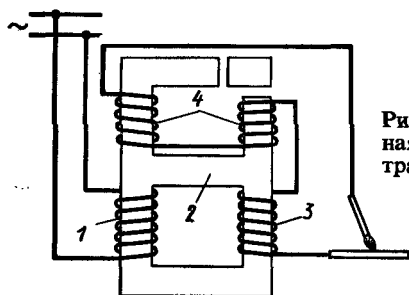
Электромагнитная схема сварочного трансформатора с встроенным реактором
